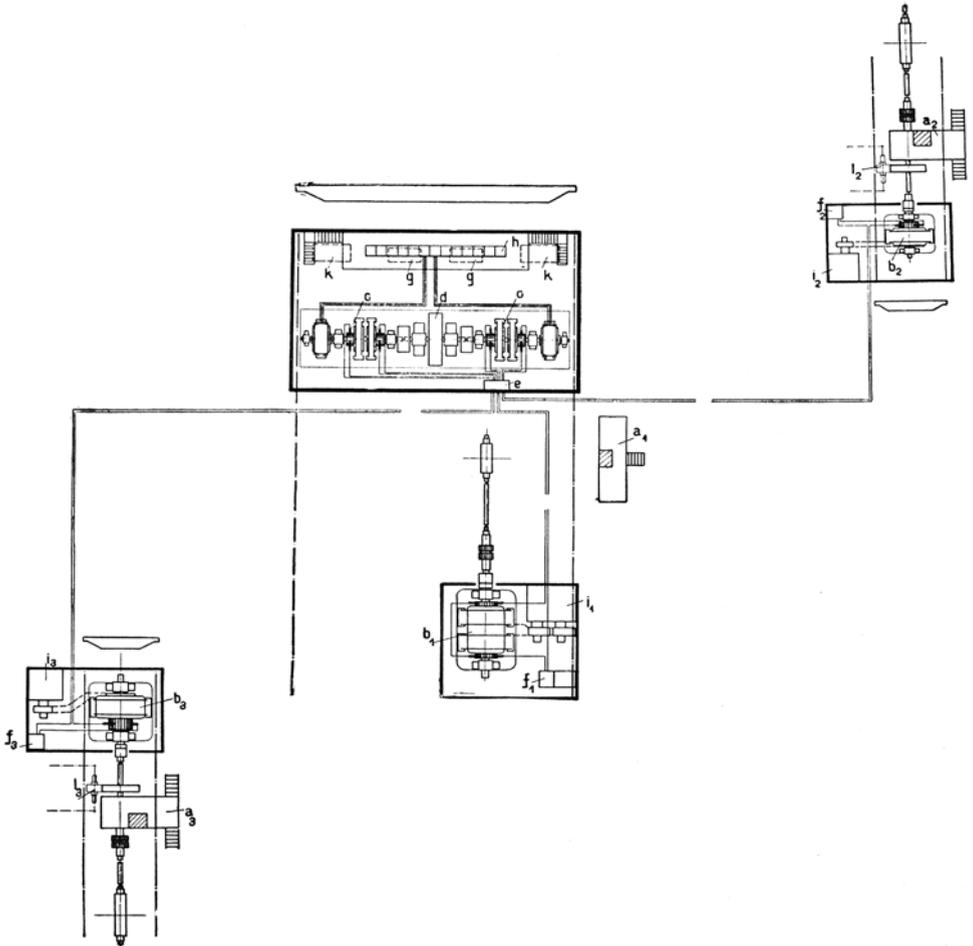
Walzwerksanlage mit elektrischem Antrieb.
